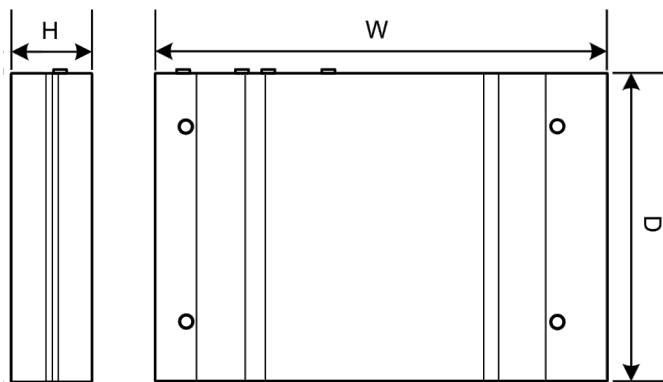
Rappresentazione schematica, dimensioni in millimetri
